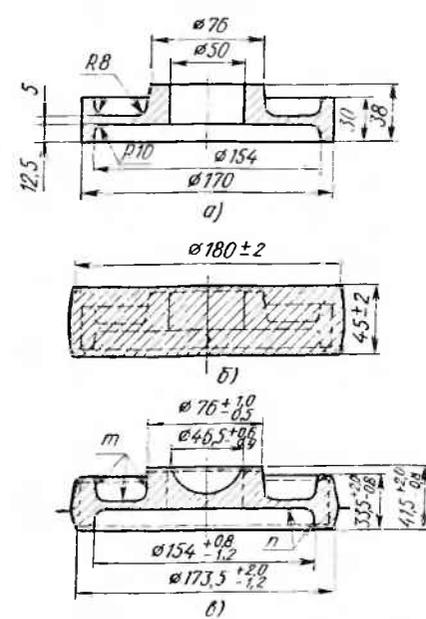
Крышка из титанового сплава (а) и поковки, полученные ковкой (б) и штамповкой (в)
